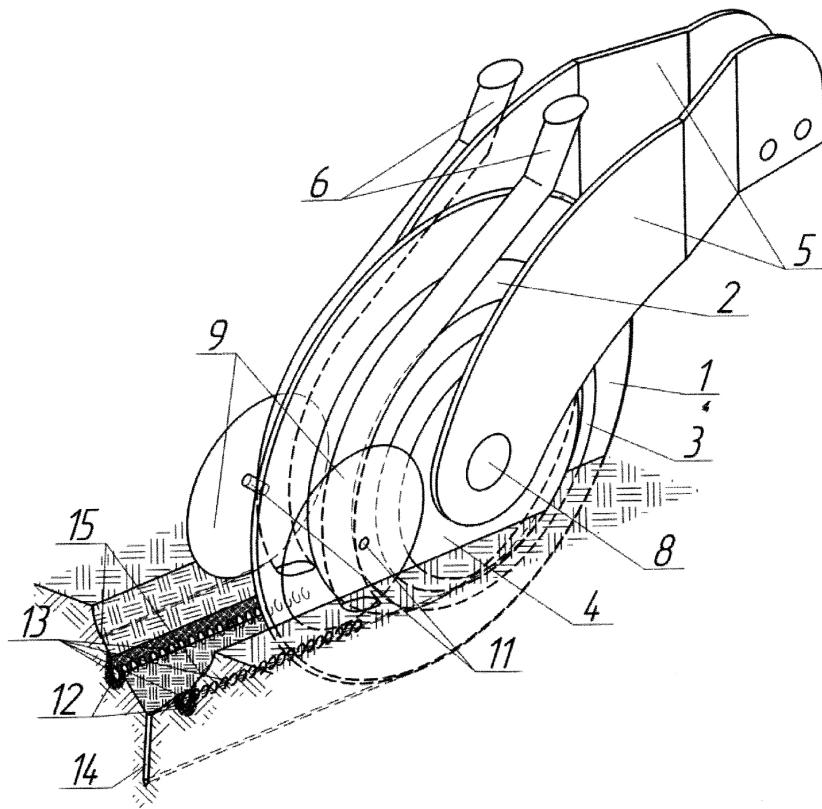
Технологическая схема работы комбинированного однодискового сошника с двухсторонними ребордами и дисковыми загортачами для узкорядного посева: 1 – плоский диск; 2 – внутренняя реборда; 3 – бороздкообразователь; 4 – наружная реборда; 5 – корпус; 6 – семянаправители; 8 – ось; 9 – сферические диски; 11 – ось; 12 – ложе; 13 – семена; 14 – щель; 15 – бороздки
